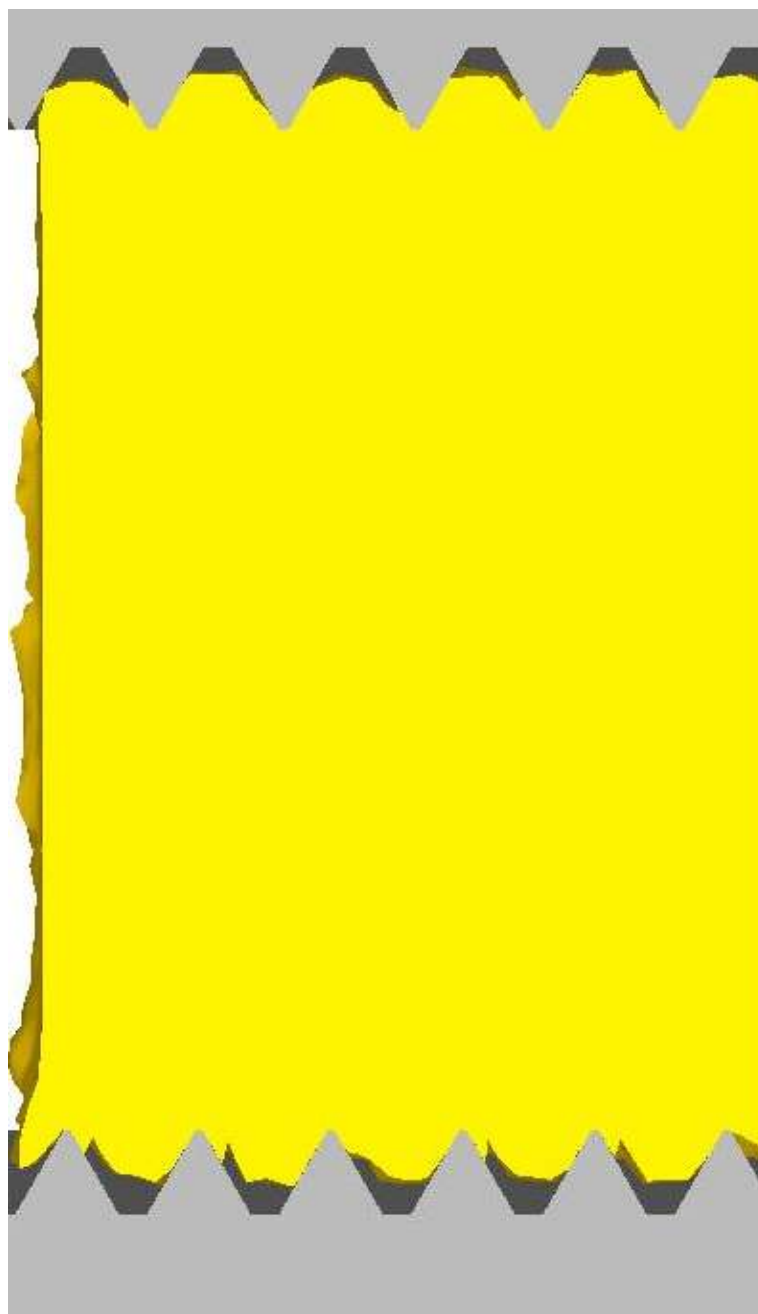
Положение инструмента и заготовки на конечном этапе процесса накатки резьбы
